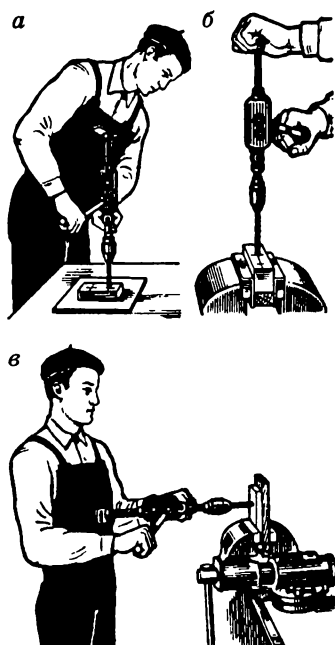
Приемы сверления ручной механической дрелью:
